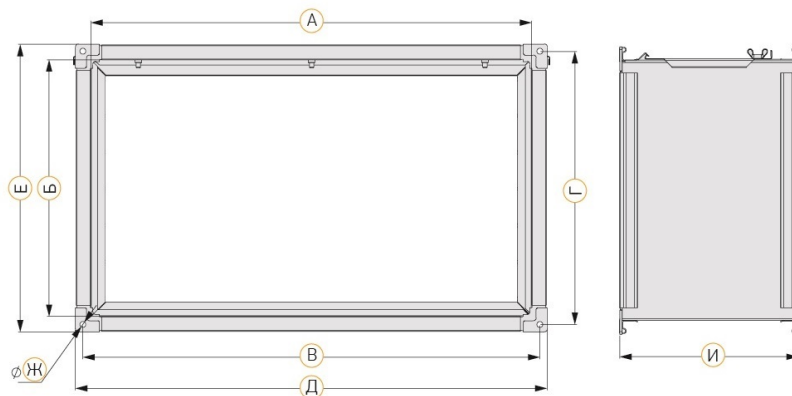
Внешний вид и основные размеры фильтров КРФ
